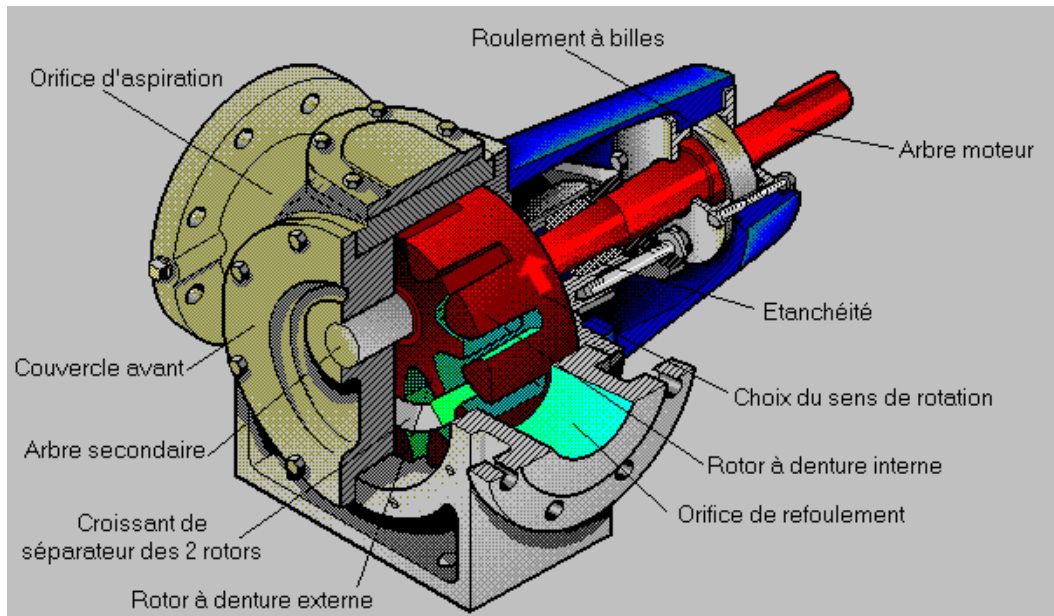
Vue écorchée d'une pompe à engrenages.
